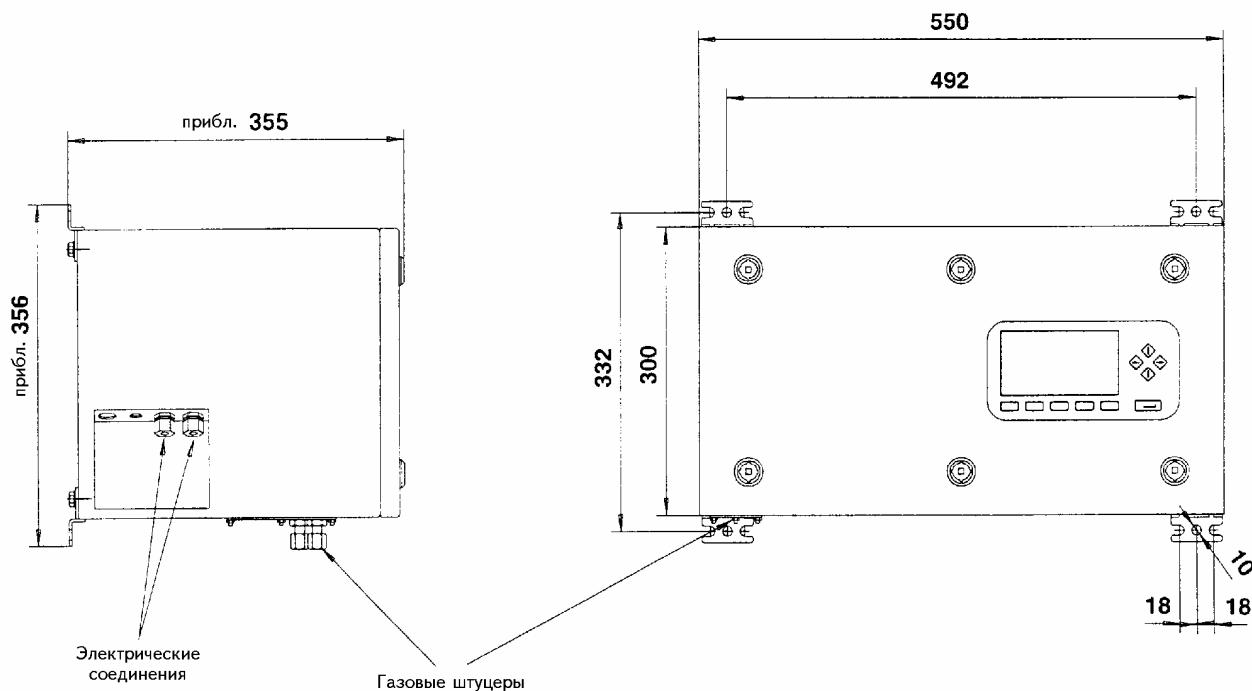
Эскиз габаритов / чертеж для засверливания для анализатора MLT 2
